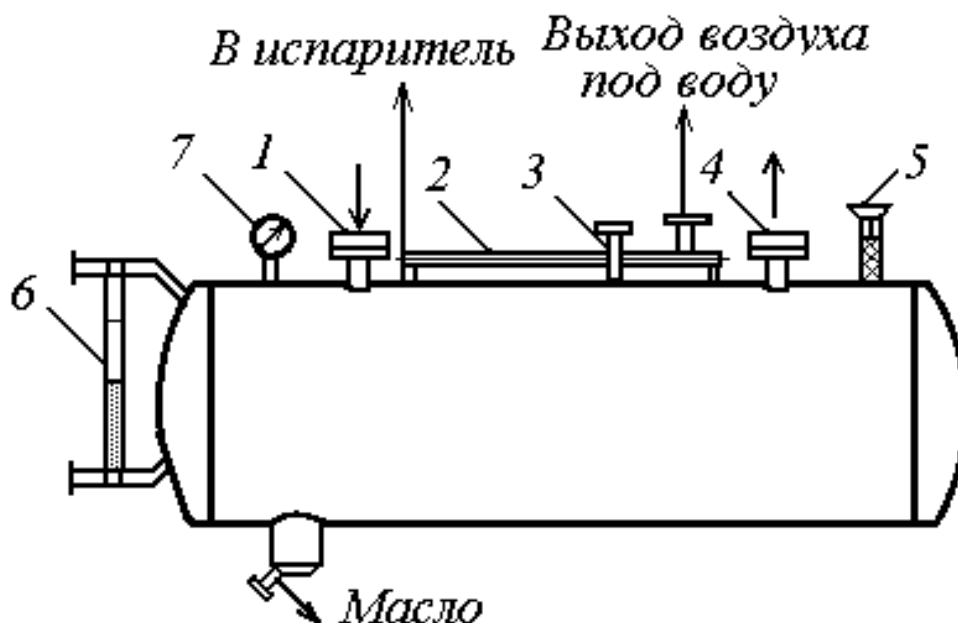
Линейный аммиачный горизонтальный ресивер:
